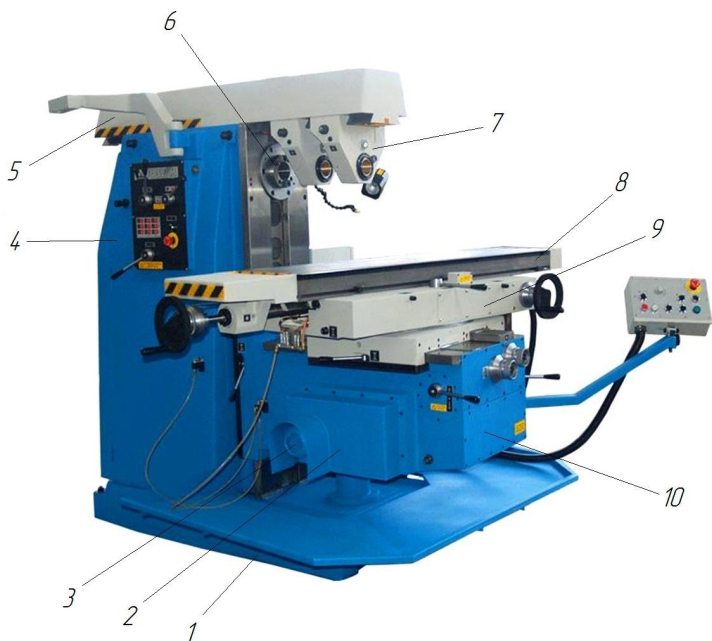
Консольный горизонтально-фрезерный станок 6Р82Г
